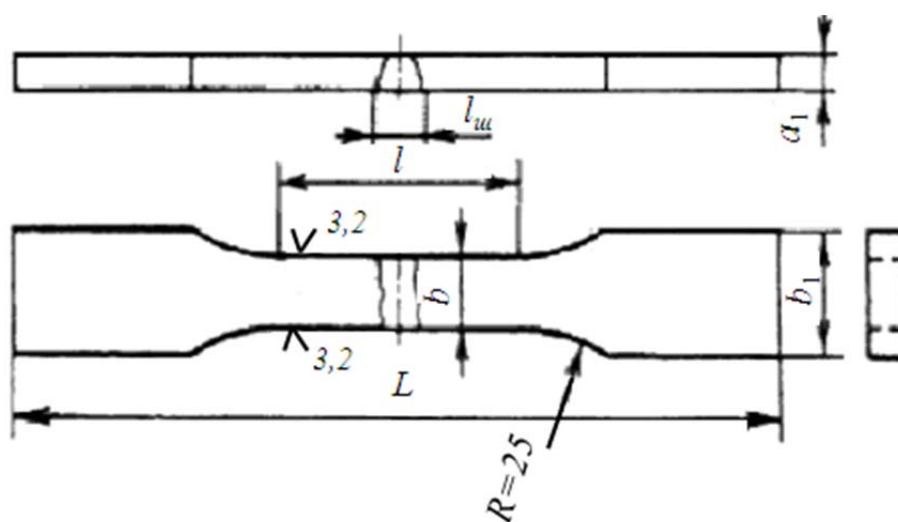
Форма зразка для випробування на статичний розтяг
